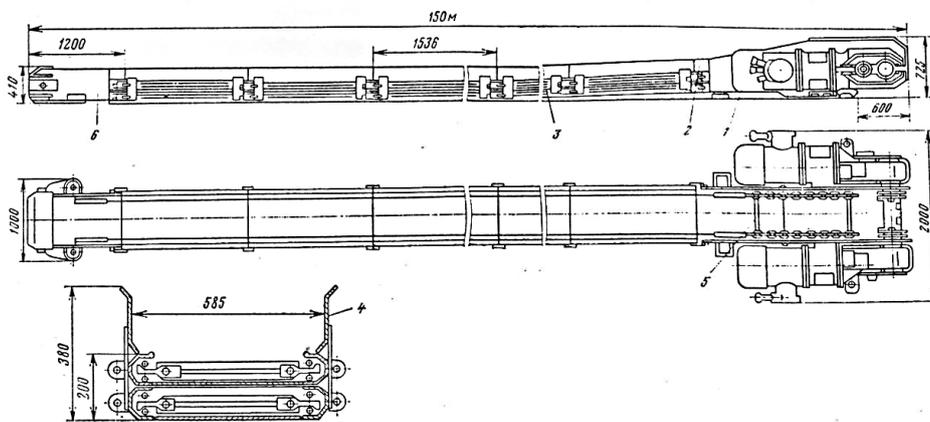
Двухцепной разборный скребокый конвейер SP-70M
